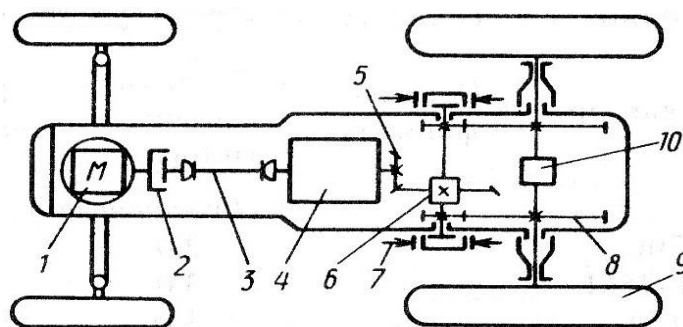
Схема механической трансмиссии колесного трактора: 1 – двигатель; 2 – муфта сцепления; 3 – карданный вал; 4 – коробка передач; 5 – главная передача; 6 – дифференциал; 7 – тормоз; 8 – конечная передача; 9 – ведущие колеса; 10 – механизм блокировки дифференциала
